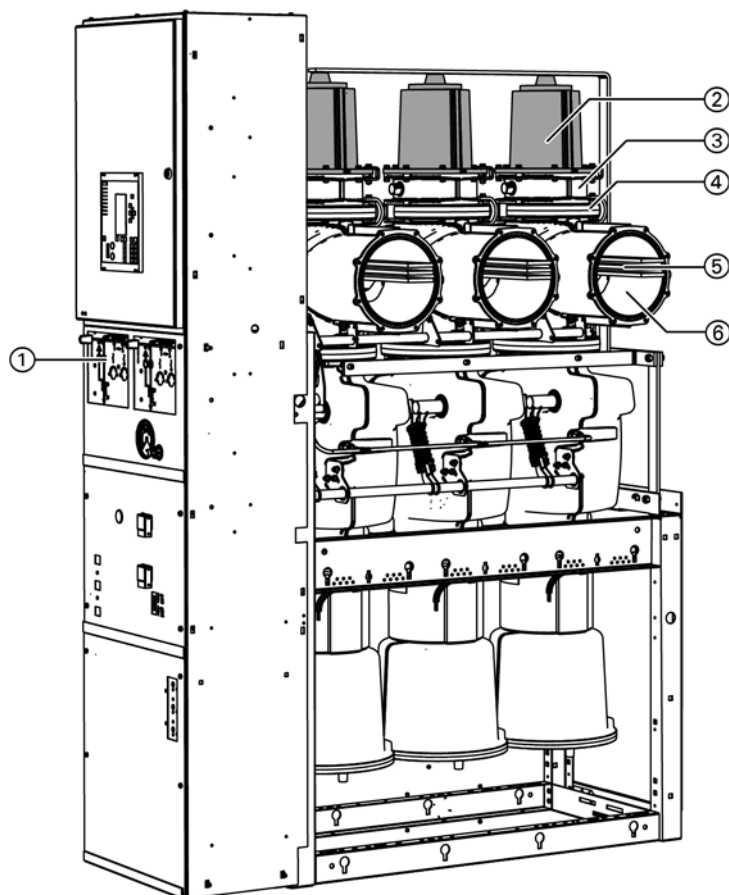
Обзор компоновки сборных шин: заземляющий выключатель сборной шины
